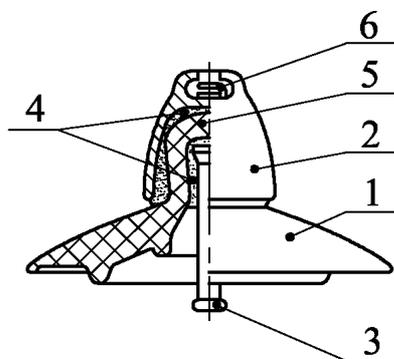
Подвесной шарнирный изолятор с конусной головкой: 1 — тарелка изолятора; 2 — чугунная шапка; 3 — стальной стержень; 4 — цементная замазка; 5 — головка изолятора; б — замок
